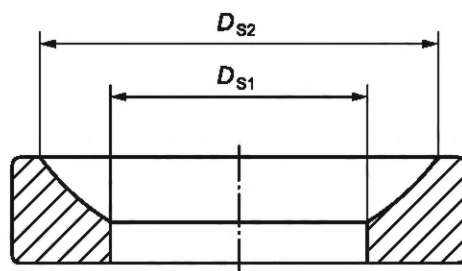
Свободное кольцо упорного шарнирного подшипника
